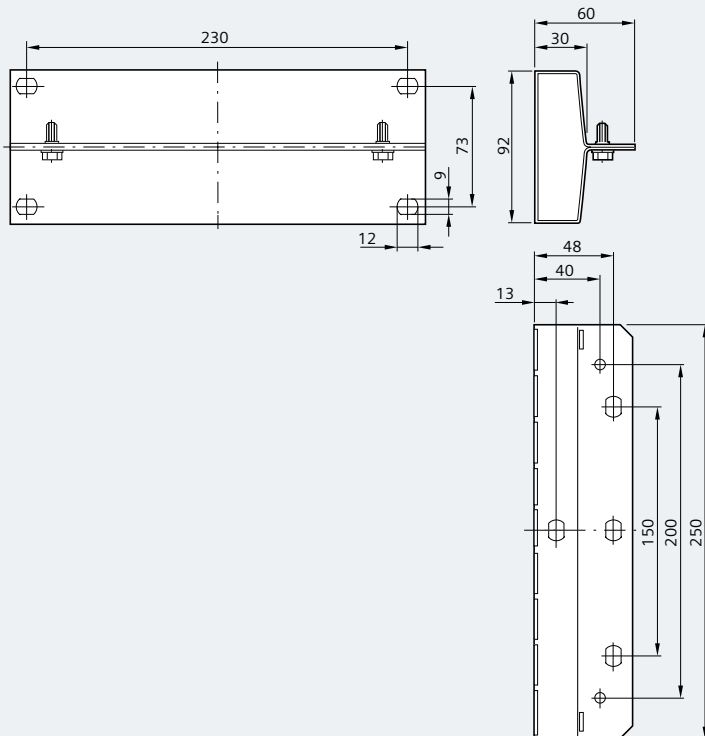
/15: Maßzeichnungen für Befestigungselemente des BD01-Systems (Maße in mm)
